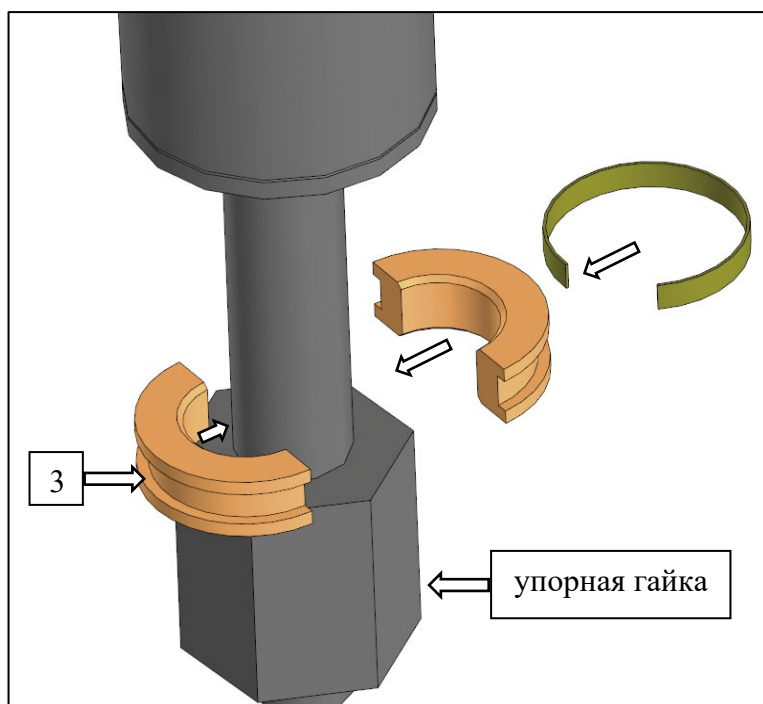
Установка упорного кольца на шток гидроцилиндра
